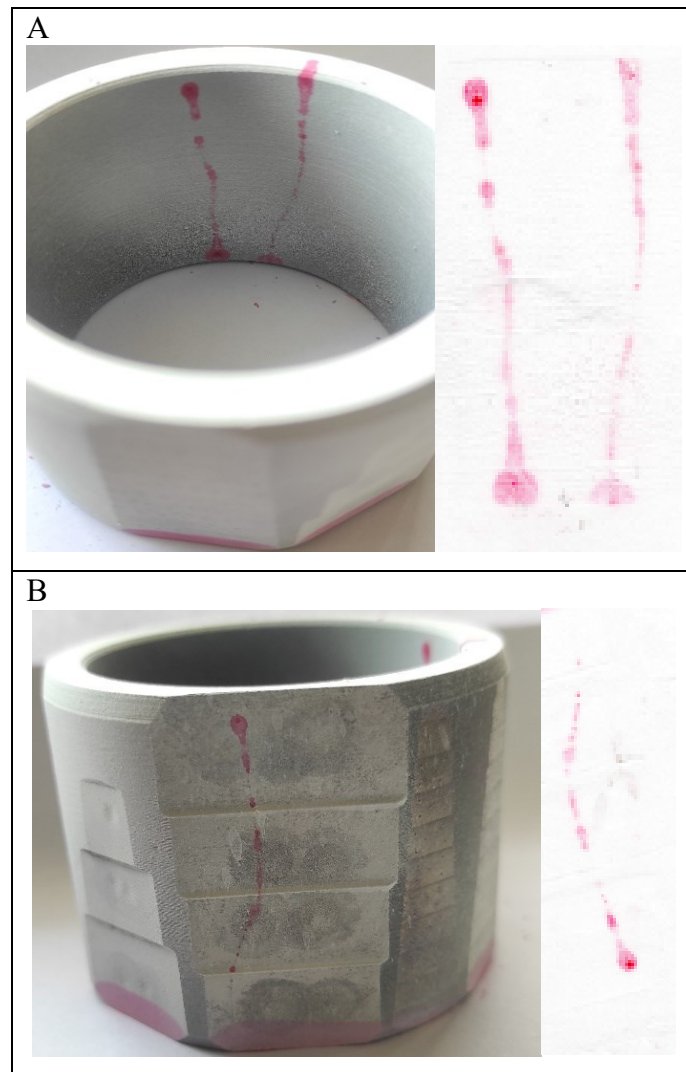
A; Fisuras en la superficie interna del buje. B; Fisura en la superficie externa del buje.
